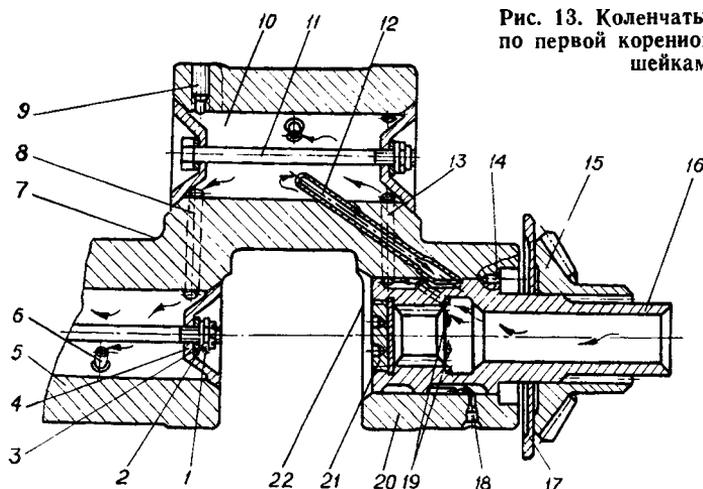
Коленчатый вал. Разрез по первой коренной и шатунной шейкам:
